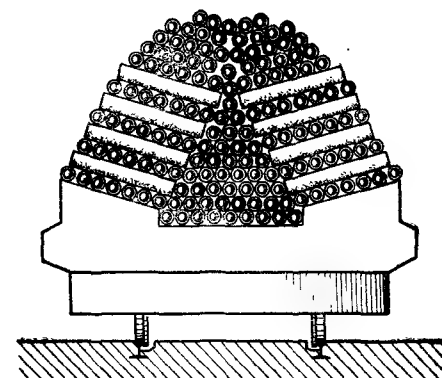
Садка дренажных труб на специализированную вагонетку туннельной печи
